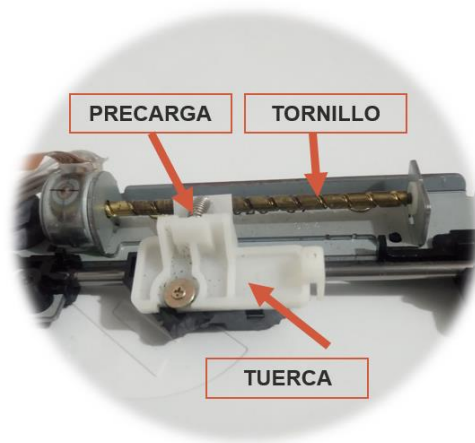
Sistema tradicional tornillo-tuerca.
